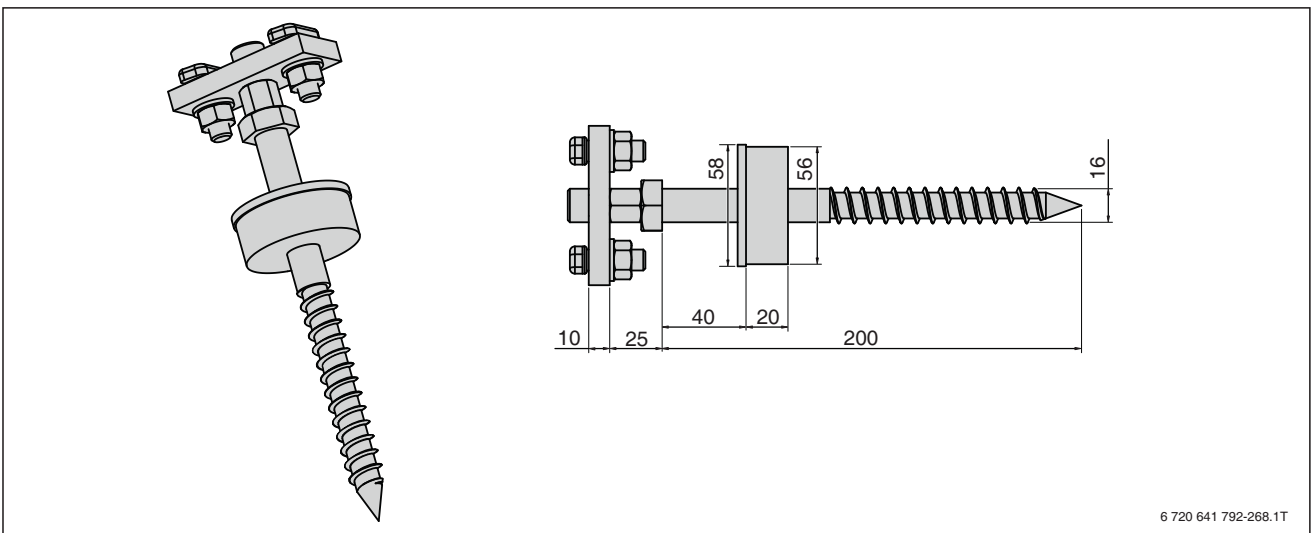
Stockschraube für Logasol SKR bei Wellplatten-Dächern
